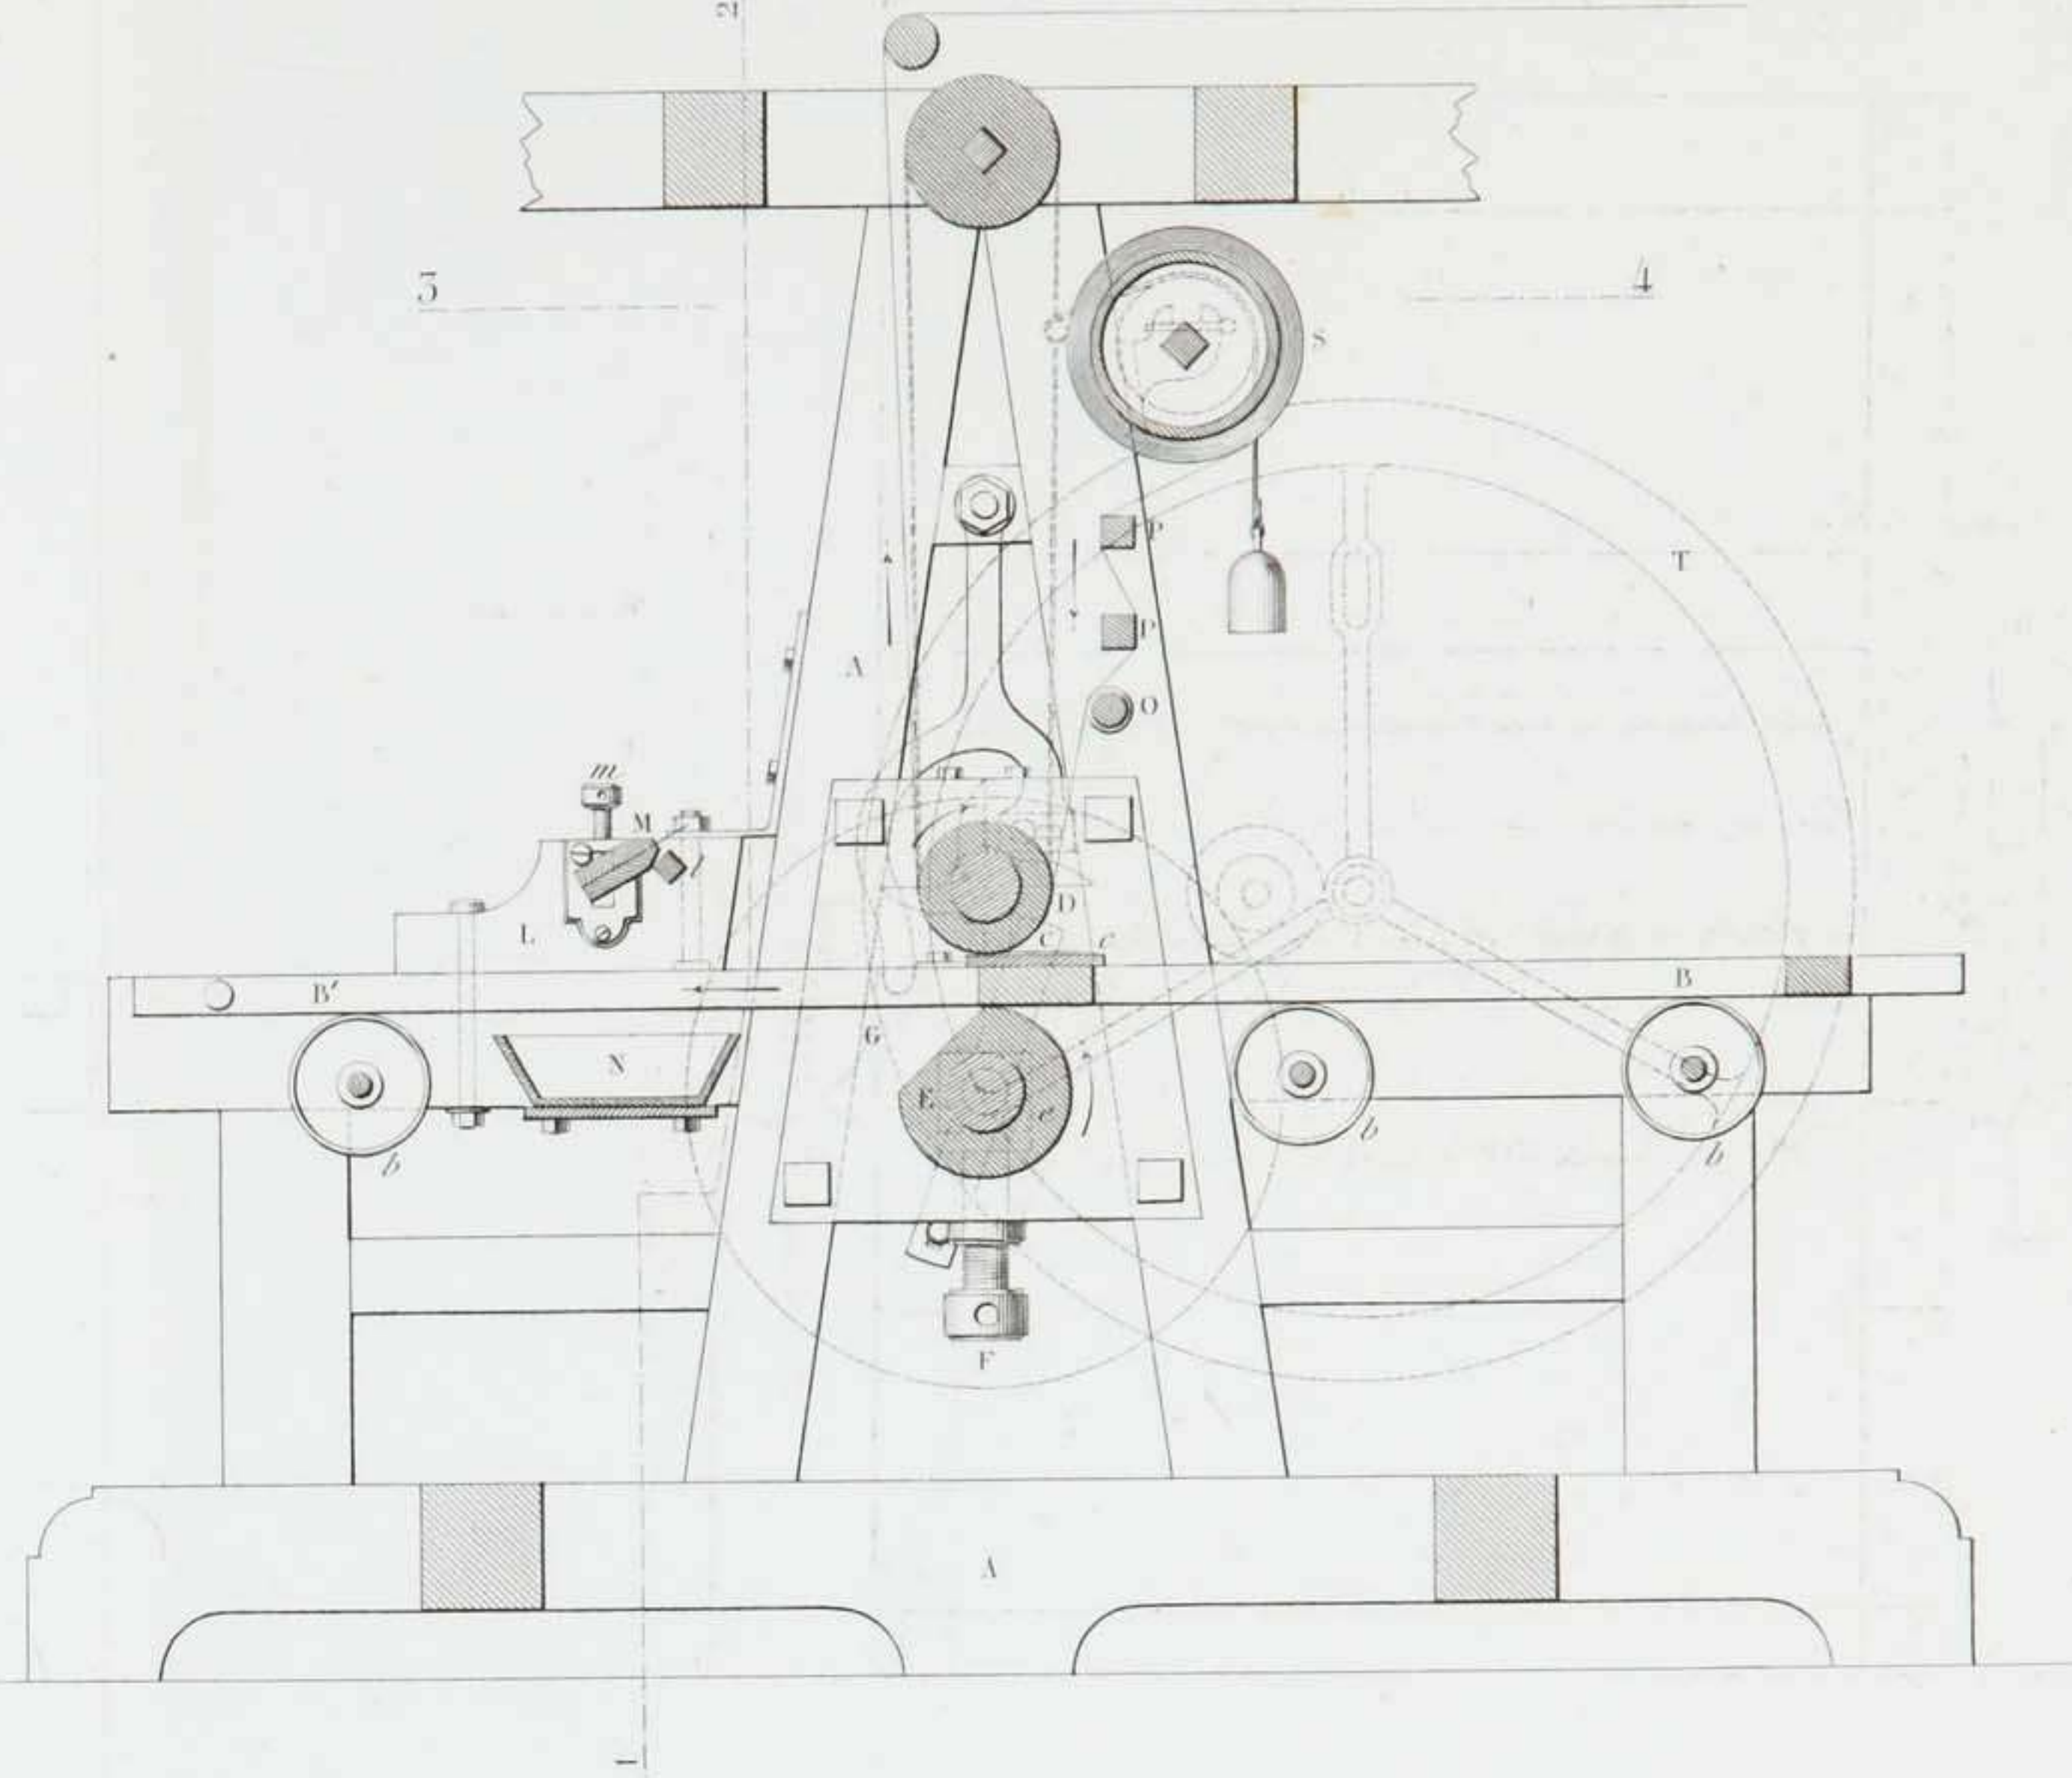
Vue extérieure du mécanisme servant à ramener la planche au rapport.
